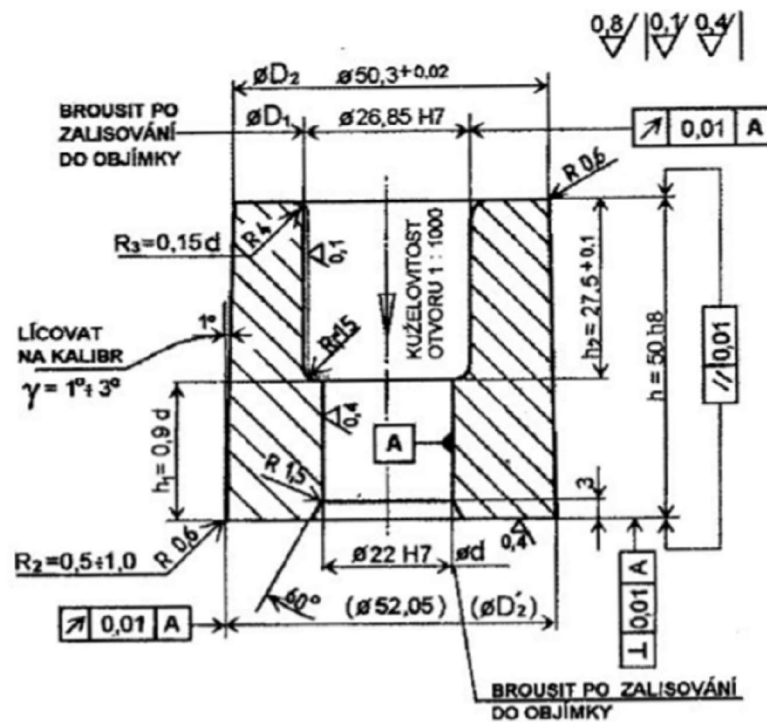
Příčné dělení průtlačnice s objímkou [2].
